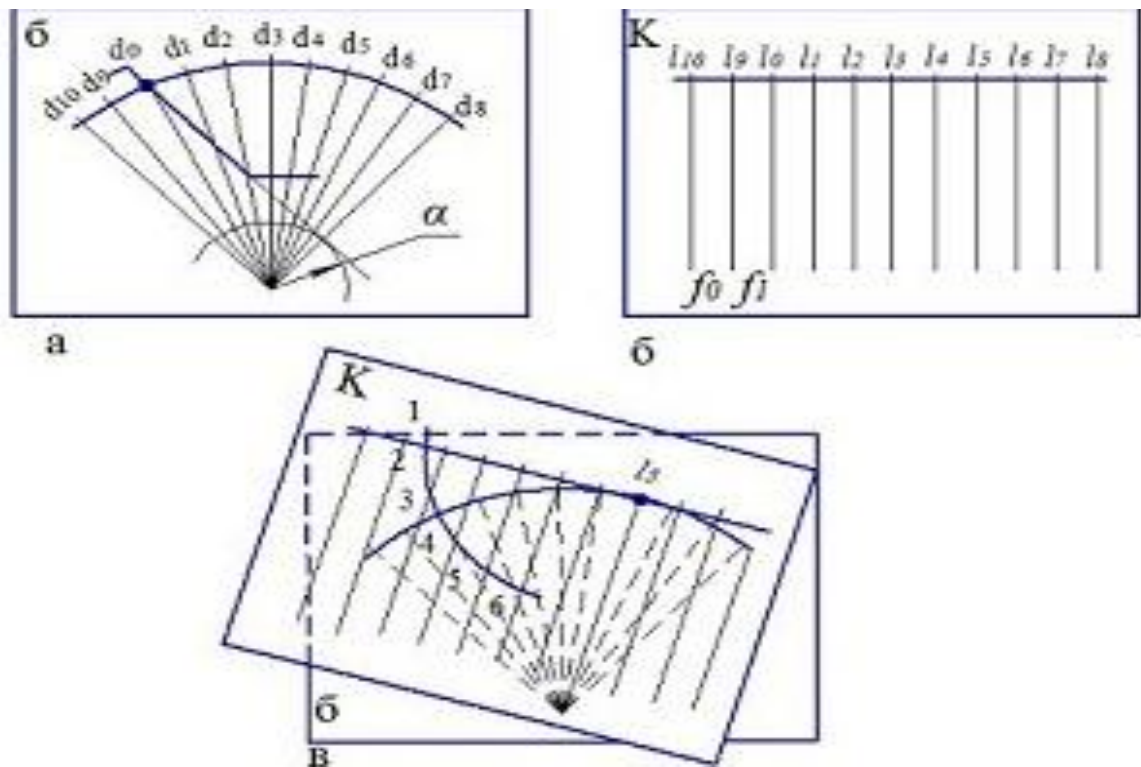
Погрешность профиля зуба фрезы (а) и боковой стороны шлица (б и в)
